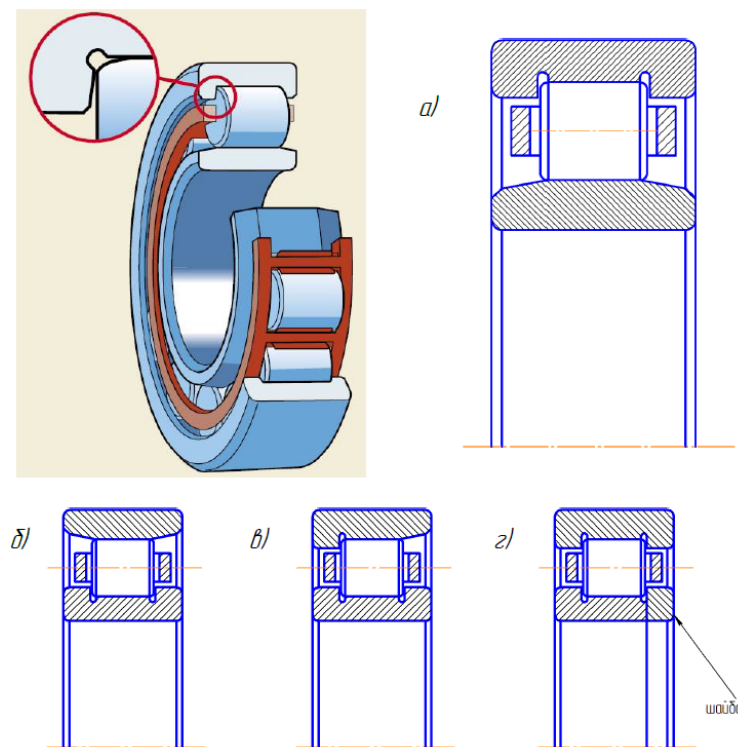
Роликовий радіальний однорядний підшипник з короткими циліндричними роликами
